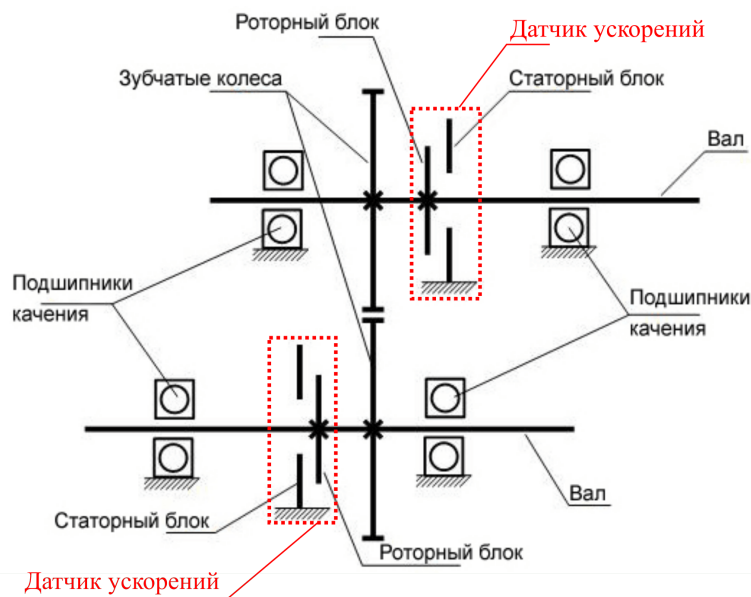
Кинематическая схема одноступенчатого зубчатого редуктора с датчиками ускорений
